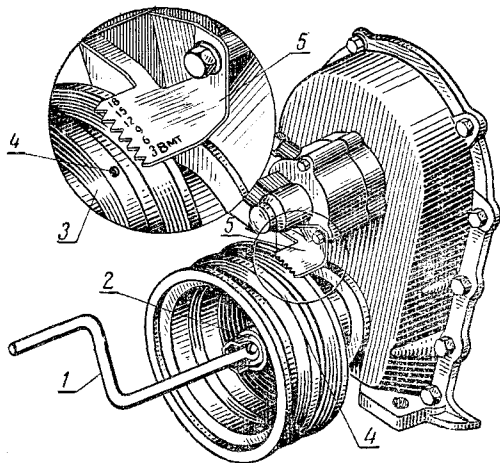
Установка поршня первого цилиндра в в.м.т. в такте сжатия двигателя ЗИЛ-130:
